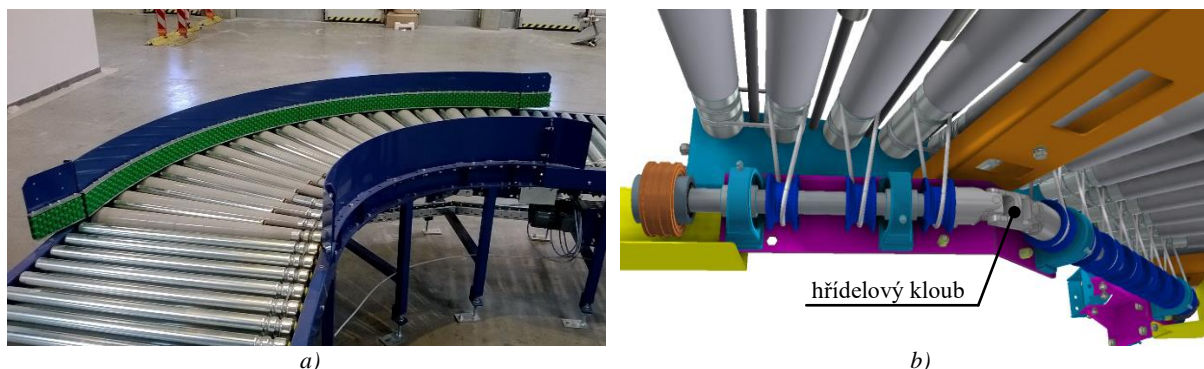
Spojení motorové a nepoháněné sekce VT driveshaft:
